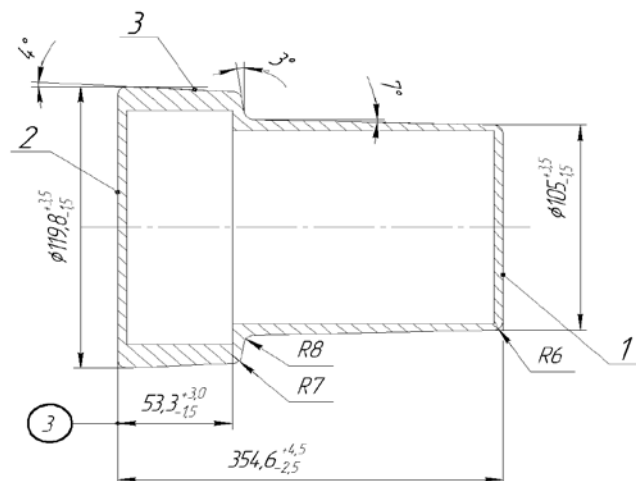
Заготовка вала з нарахованими припусками і допусками
